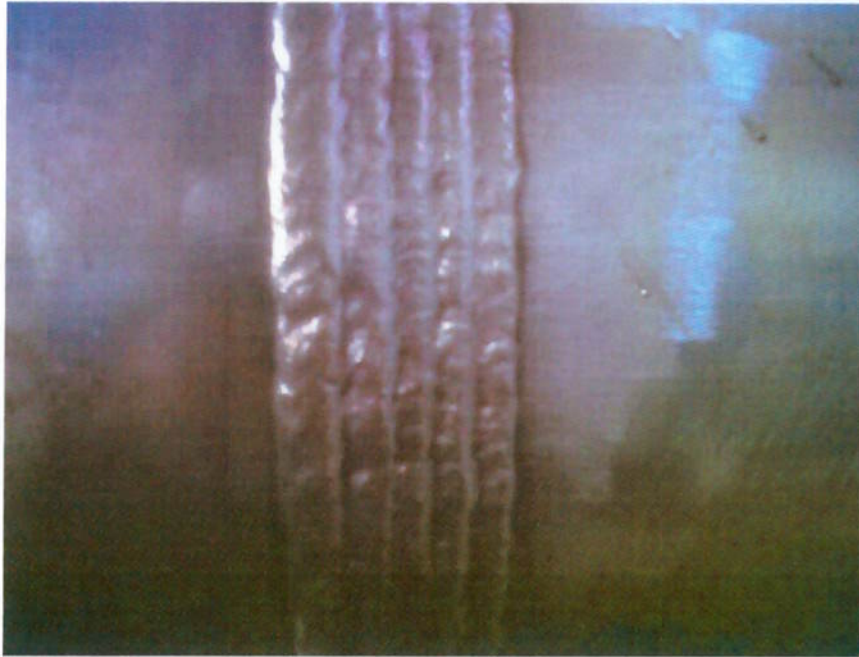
Junta devidamente soldada e pronta para ensaio visual.
